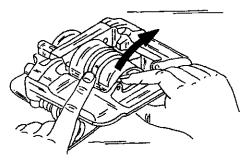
Установка пылезащитного кольца в поршне и отверстии цилиндра. При этом поршень поворачивать в направлении стрелки.
